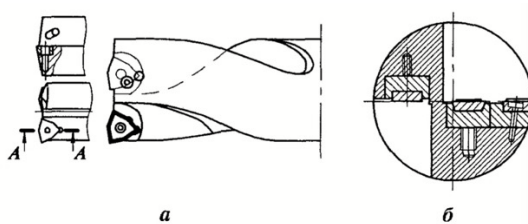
Конструкція свердел з непереточуваними пластинами твердого сплаву
